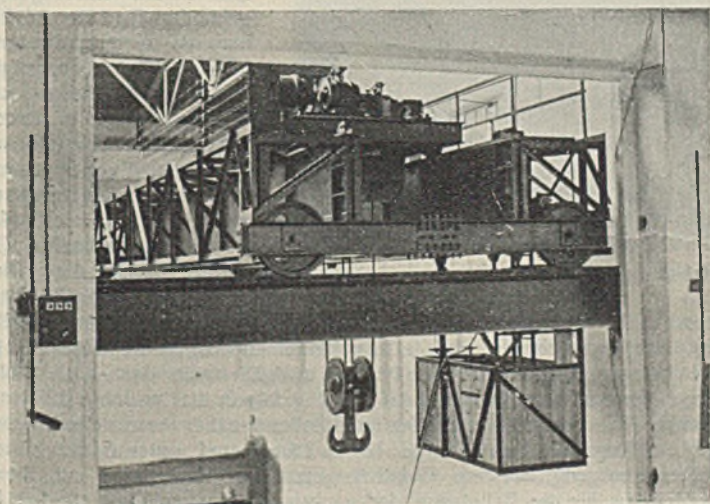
In Österreich ganz geschweißter Laufkran, 12 m Spannweite, 20 t.
